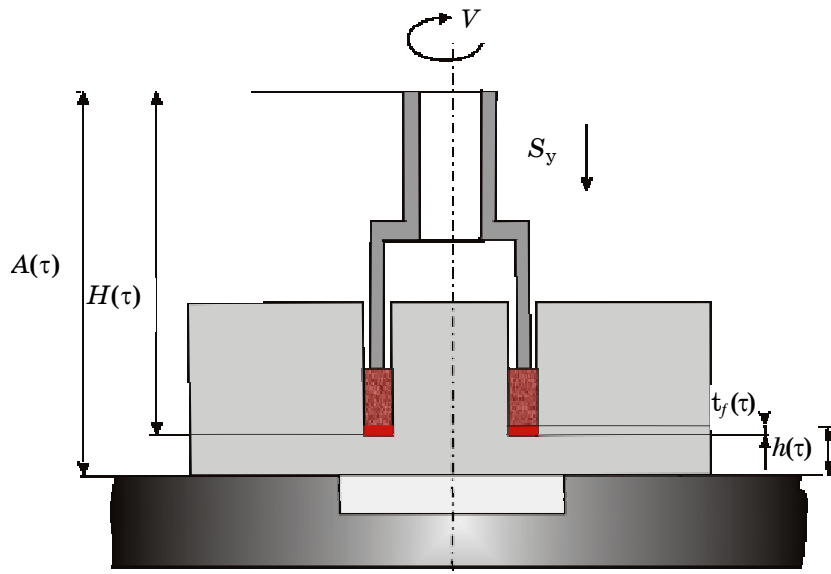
Схема взаимодействия алмазного сверла и заготовки
